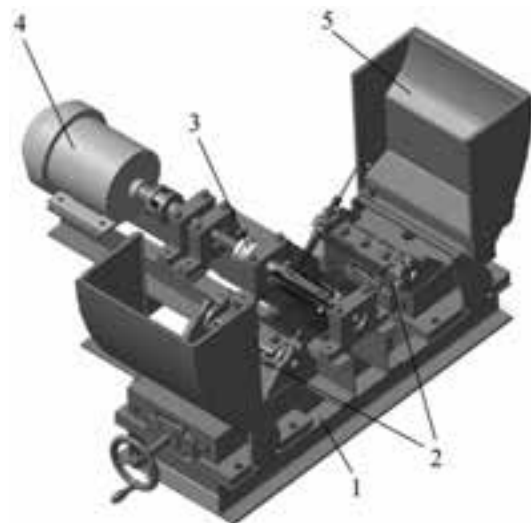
Схема расположения основных узлов стенда УИН: 1 — рама; 2 — суппорт; 3 — барабан; 4 — электродвигатель; 5 — двери защитного кожуха
